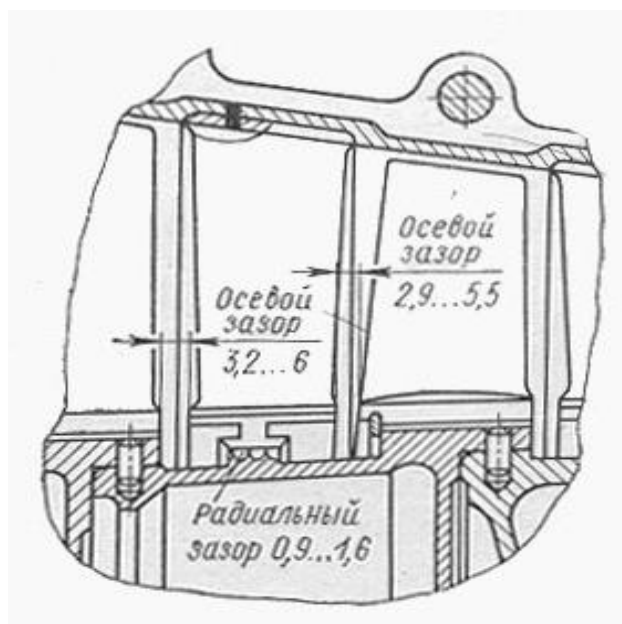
Двустороннее крепление направляющих лопаток двумя цапфами.
